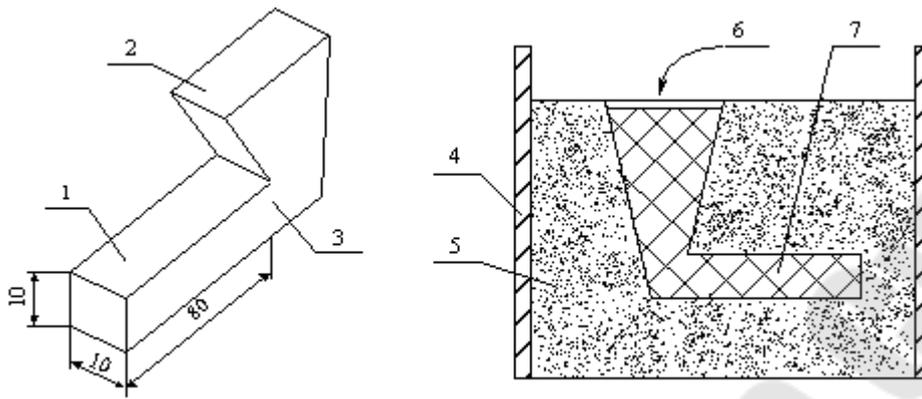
Металлическая форма для изготовления испытуемого образца
